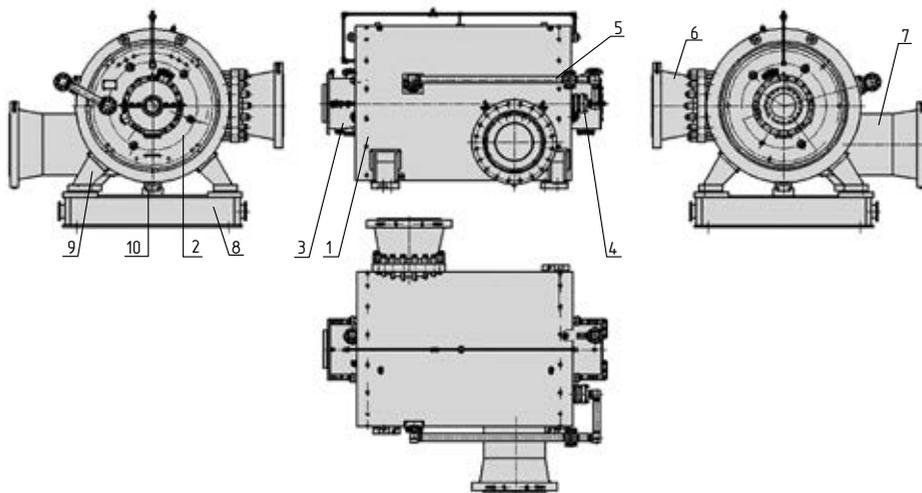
Общий вид компрессора: 1 – цилиндр; 2 – пакет; 3 – кожух опорного подшипника; 4 – кожух опорно-упорного подшипника; 5 – трубопровод; 6 – всасывающий патрубок; 7 – нагнетательный патрубок; 8 – рама фундаментная; 9 – опора; 10 – наварыш
